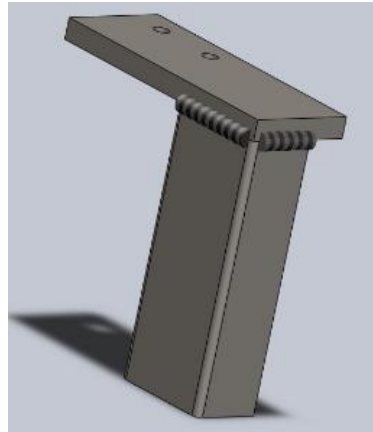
Método de ensamble es por cordón de soldadura
